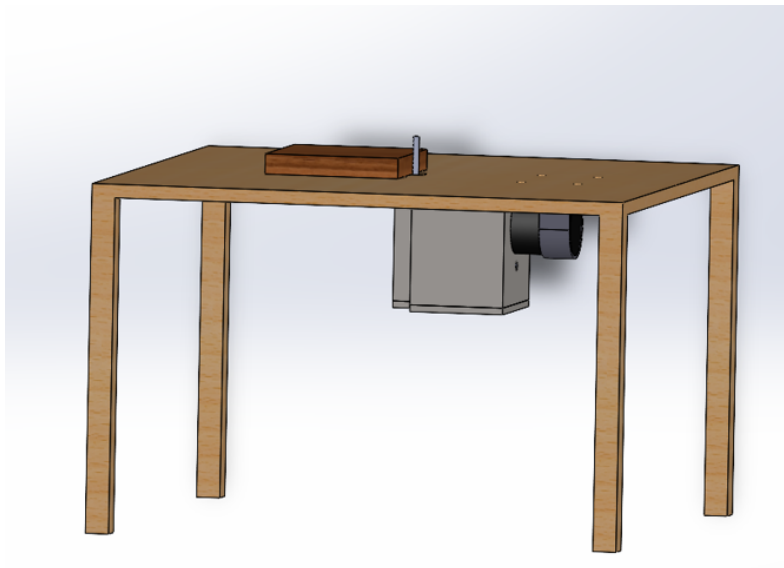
Vue de face de l'ensemble scie-table (vue frontale)
